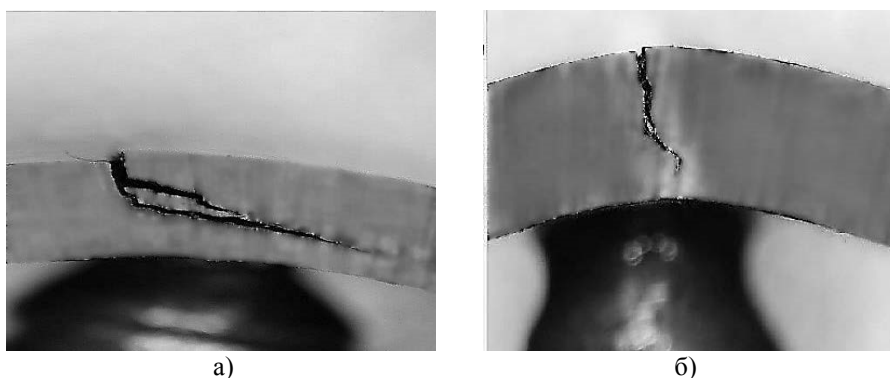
Вид трещин с торца образцов: а - КП; б - закалка из МКИТ + отпуск
